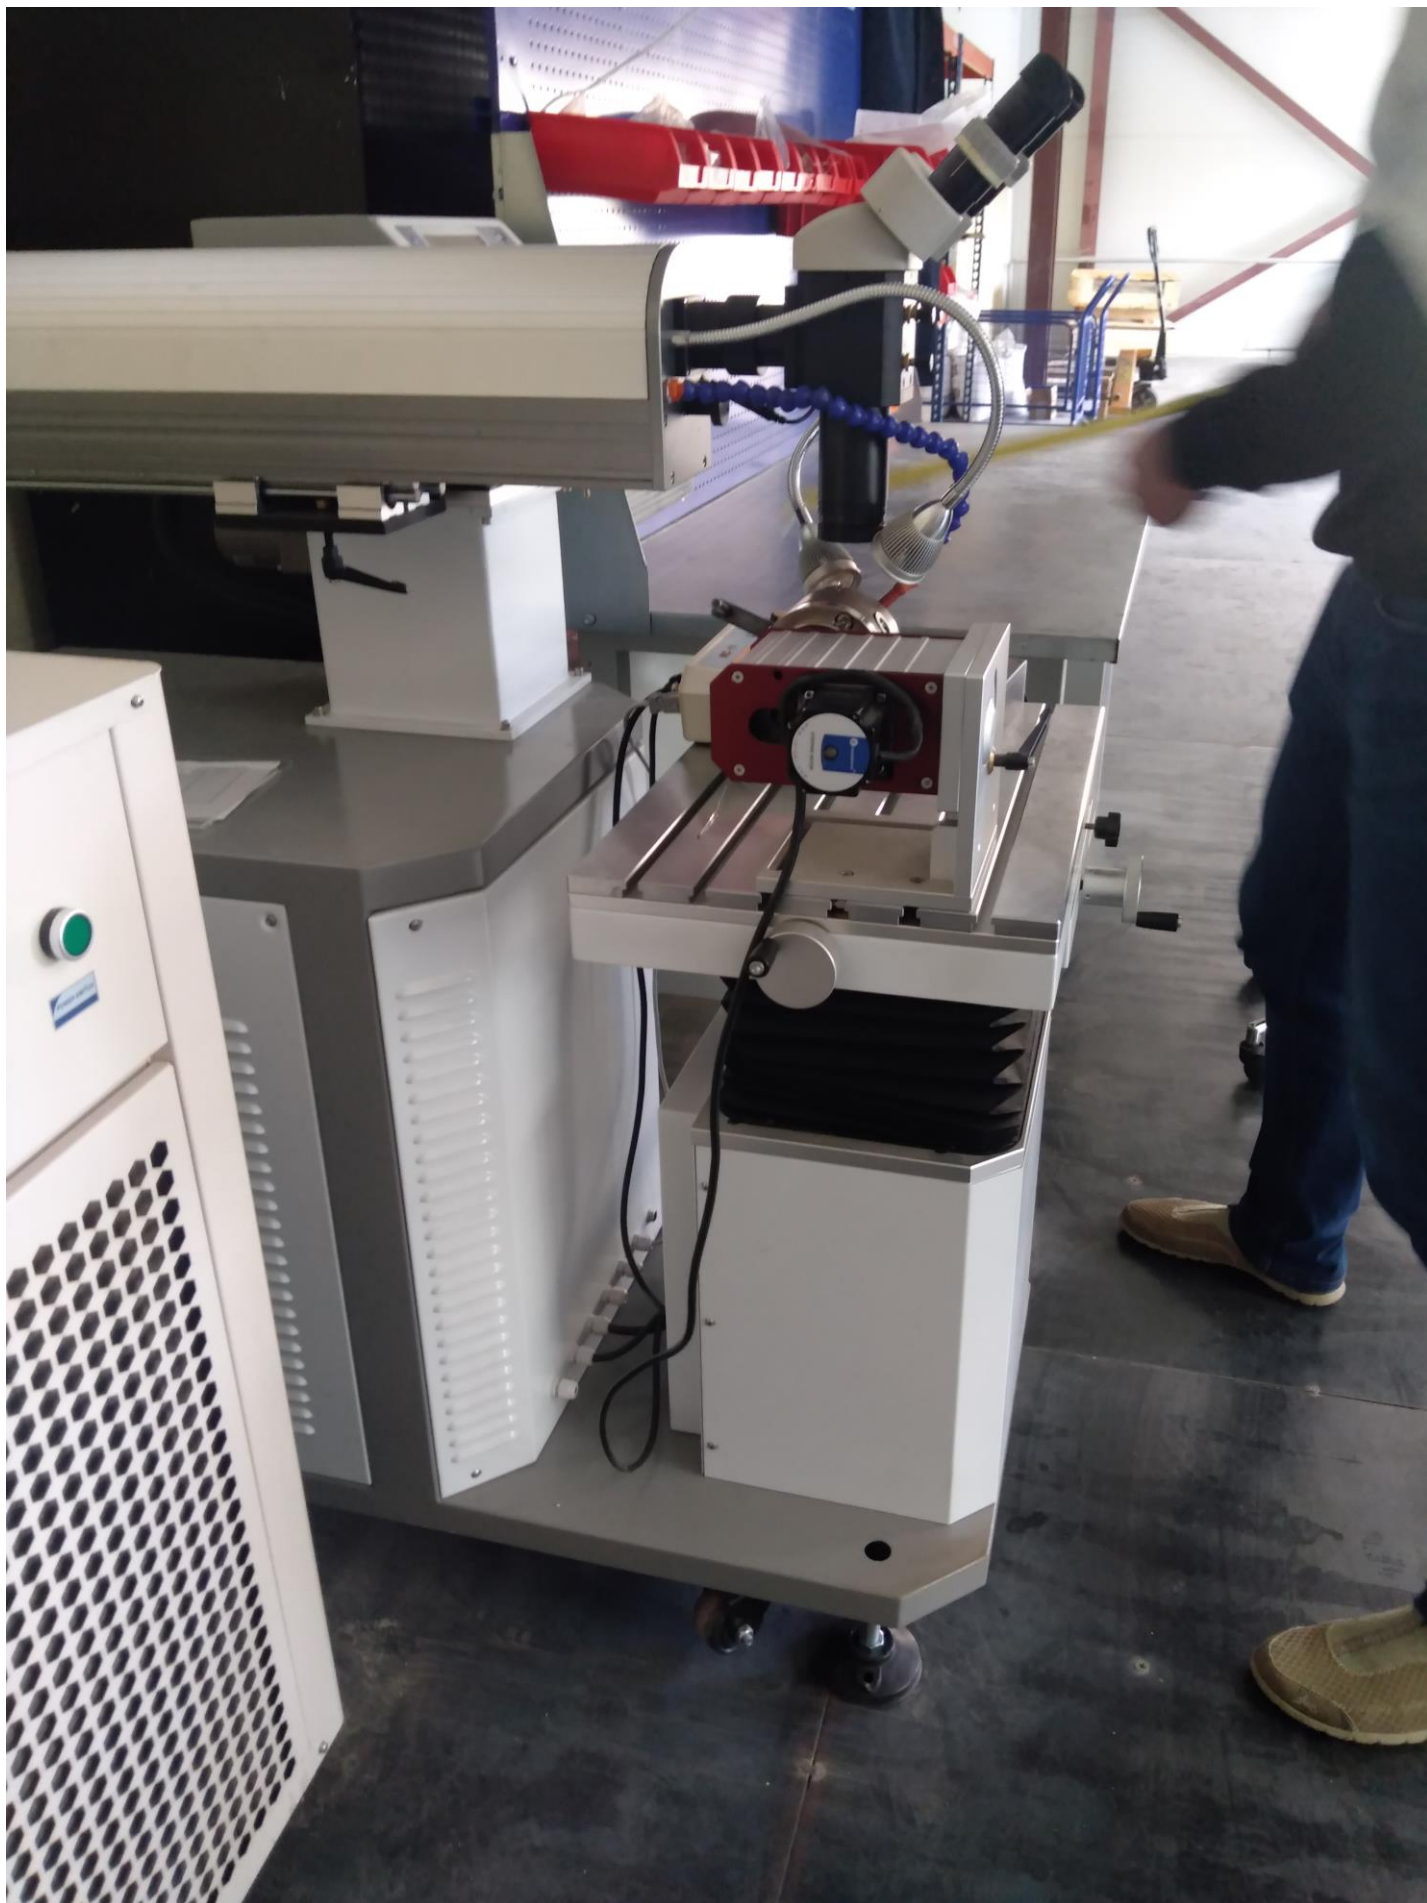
Установка лазерной сварки (вид сбоку)
